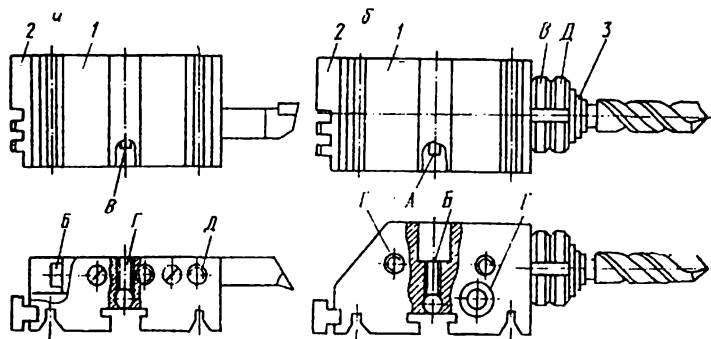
Інструментальний блок для закріплення нерухомих інструментів на токарних верстатах при їх автоматичній заміні:
